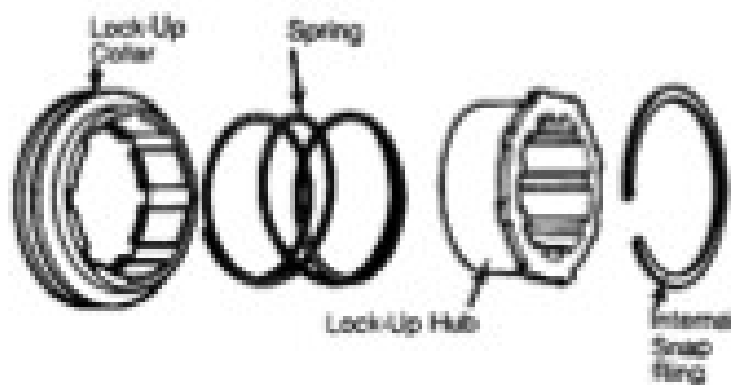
Vista explodida do conjunto de bloqueio 2WD/4WD.
